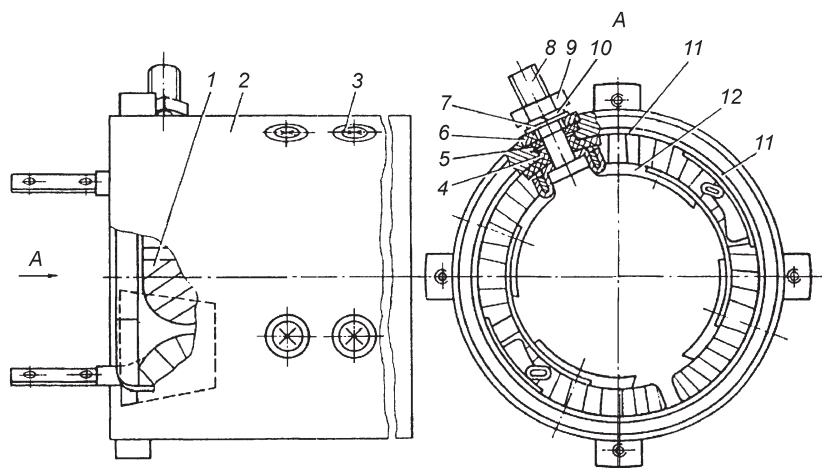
Корпус стартера СТ142-Б в сборе:
